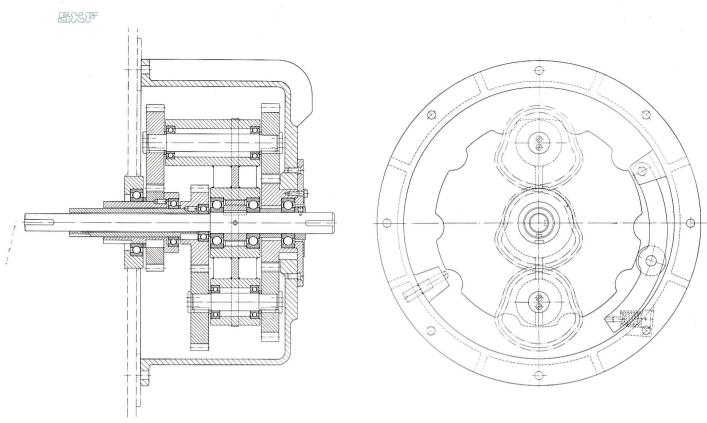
Disposición de rodamientos para el engranaje planetario según la fig. 1
